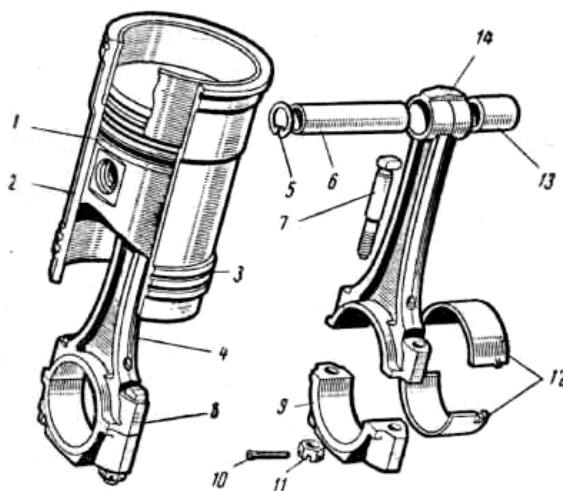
Шатунно-поршнева група в зборі з гільзою циліндра та елементи конструкції шатуна: 1 – поршень; 2 – гільза циліндра; 3 – гумові кільця ущільнювачів; 4 – стрижень шатуна; 5 – замочне кільце; 6 – поршневий палець; 7 – шатунний болт; 8 – нижня головка шатуна; 9 – кришка нижньої головки шатуна, 10 – шплінт; 11 – гайка шатунного болта; 12 – вкладиші нижньої головки шатуна; 13 – втулка верхньої головки шатуна; 14 – верхня головка шатуна.
